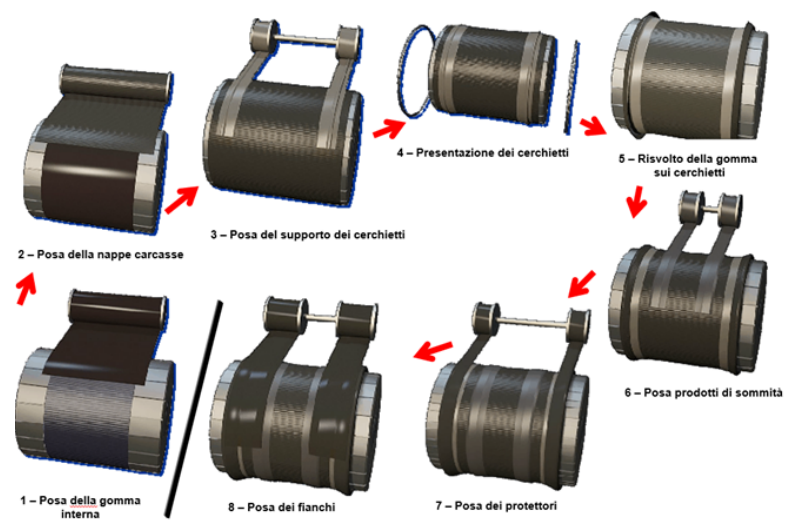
Prima fase di assemblaggio di uno pneumatico
